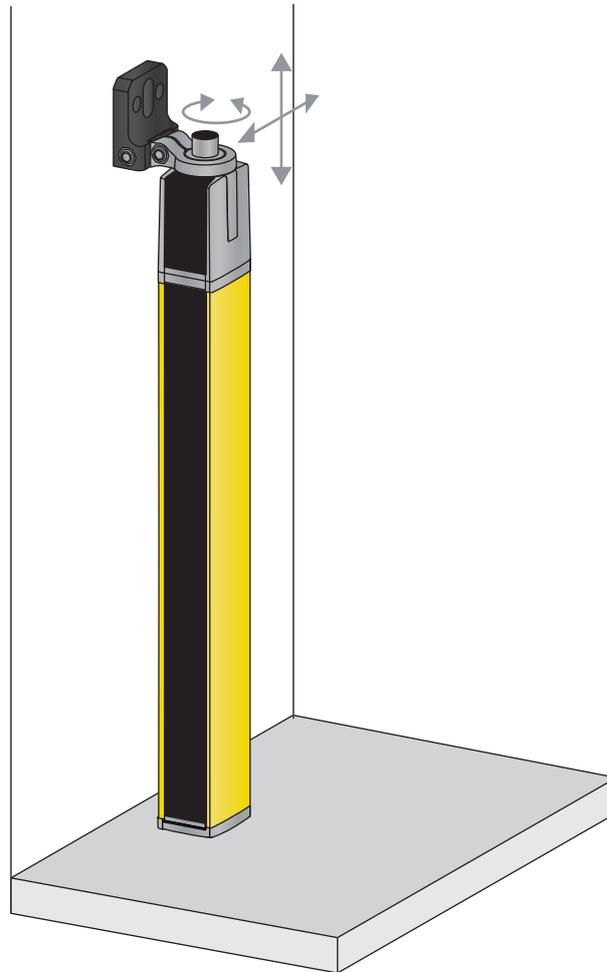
Befestigung direkt auf dem Maschinentisch
